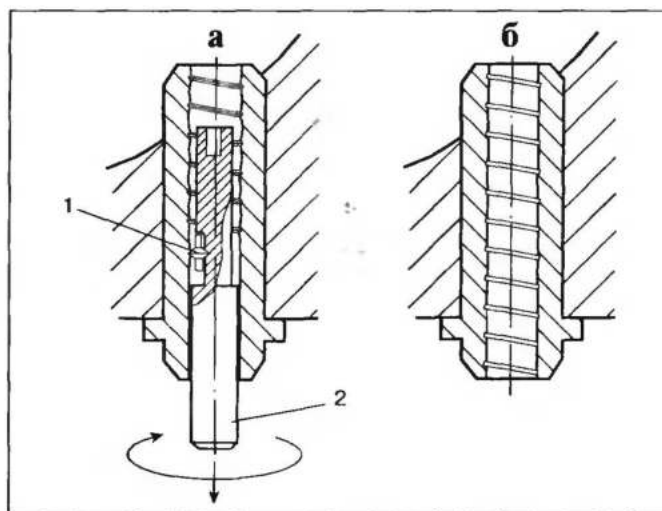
Ремонт отверстия направляющей втулки клапана с помощью специального приспособления - раскатки (роллера): а — нарезание внутренней резьбы; б — отверстие после обработки разверткой в размер стержня клапана; 1 — ролик из твердого сплава; 2 — роллер
